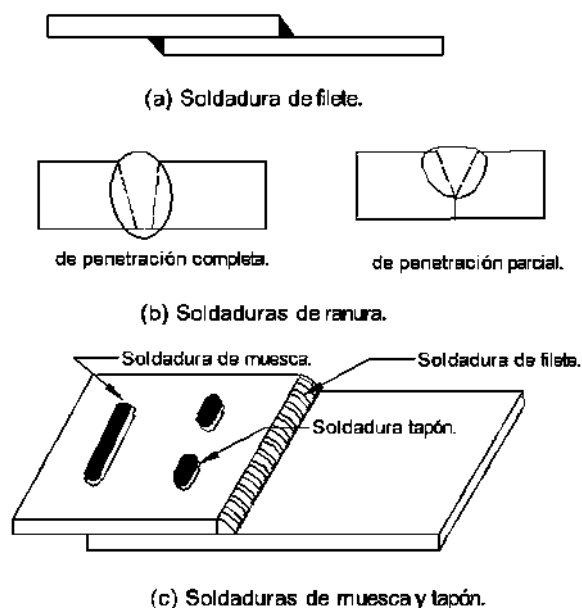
7 Tipos de soldadura (Modificado de Jack, C. & Stephen, F. 2012).
